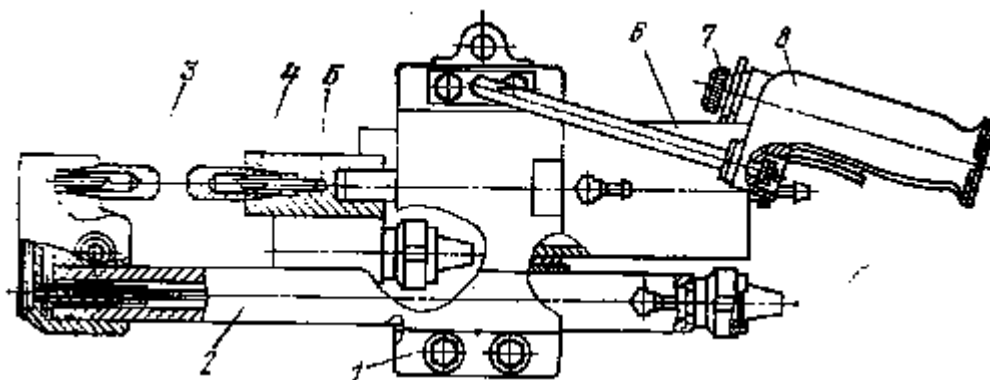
Сварочные клещи КТП-8-2
